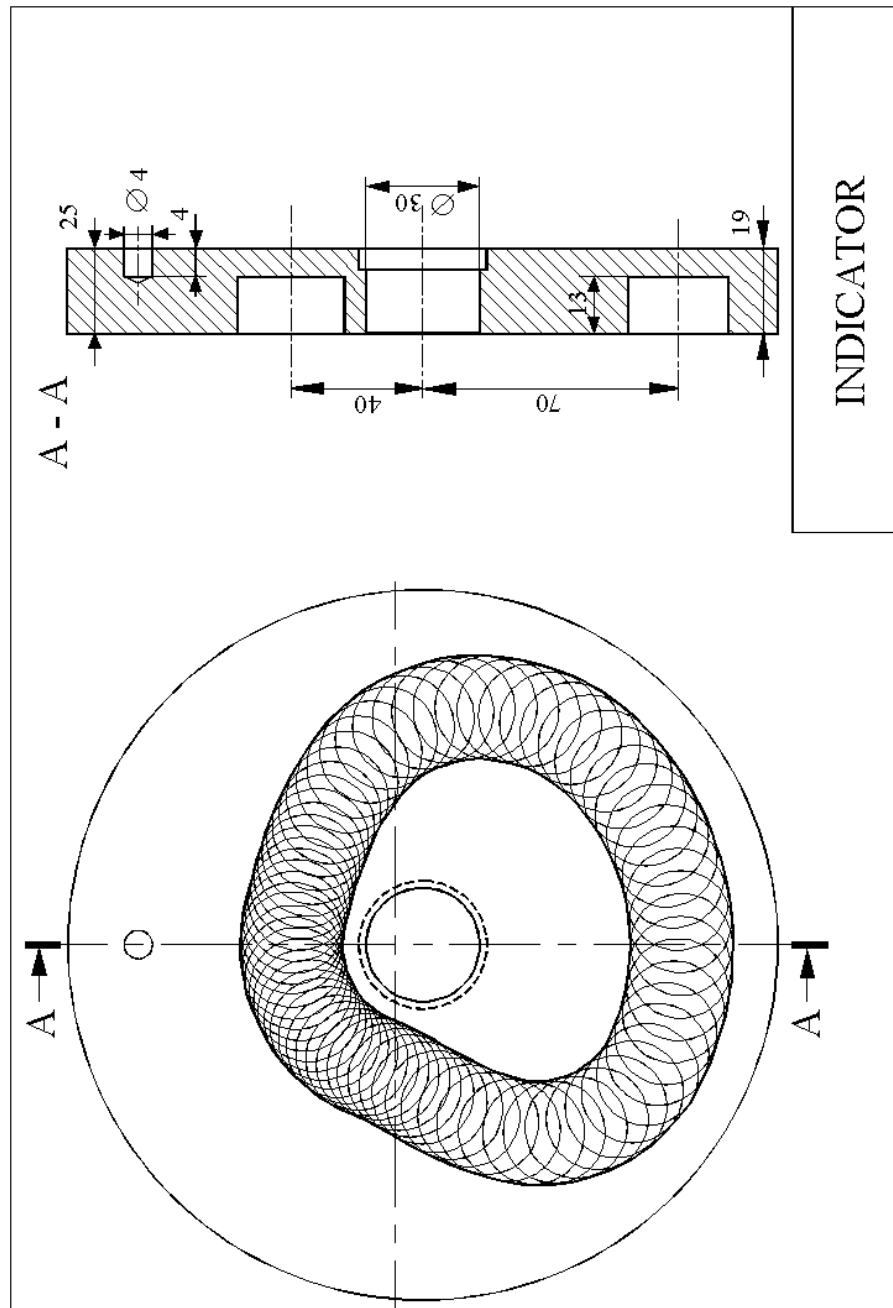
Desen de execuție a unei came cu canal frontal [3.13].
